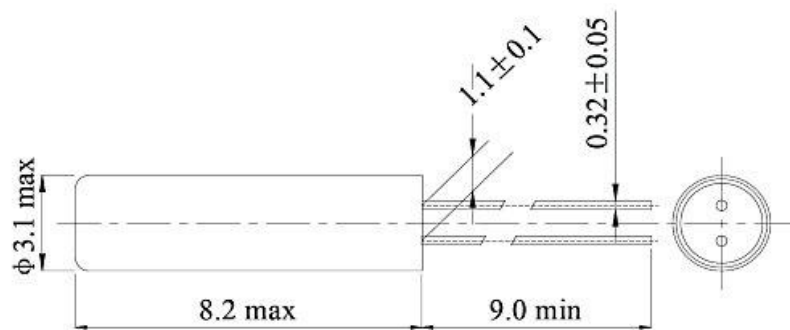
Ескіз кварцового резонатора в корпусі DT38
